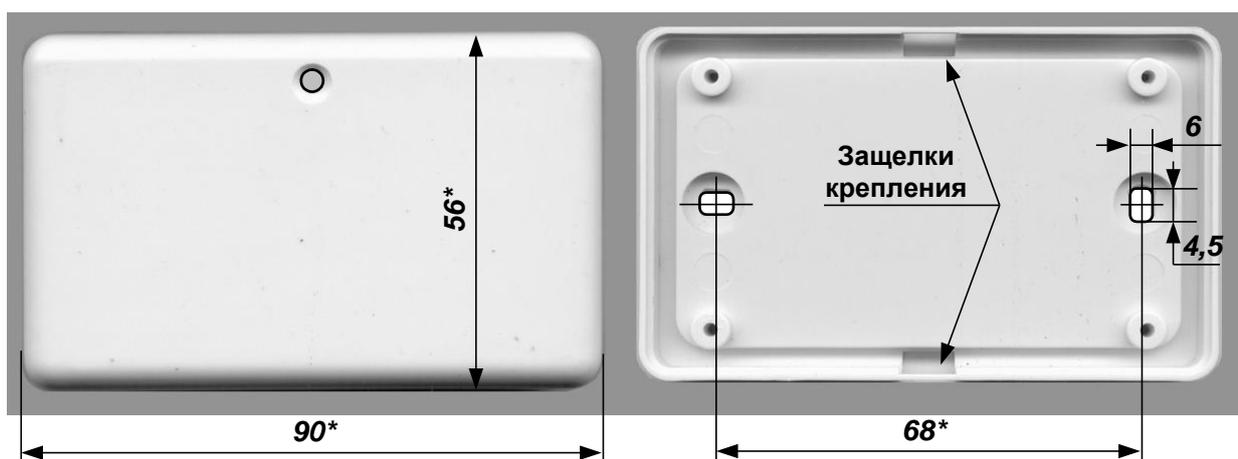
Габаритные и присоединительные размеры ИСМ5 в корпусе
